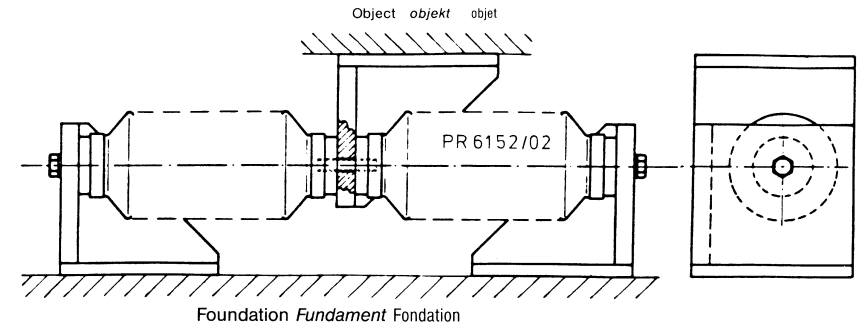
Fixation des stabilisateurs horizontaux PR 6152/02 entre consoles
